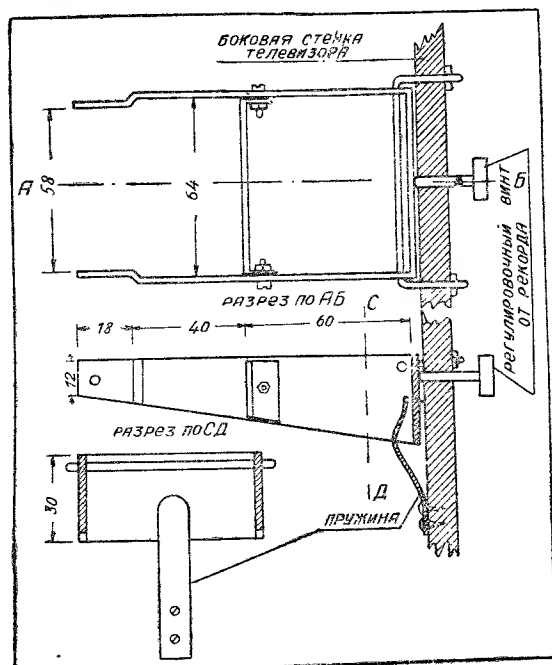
Кронштейн крепления мотора для диска Нипкова с двумя оборотами спирали
